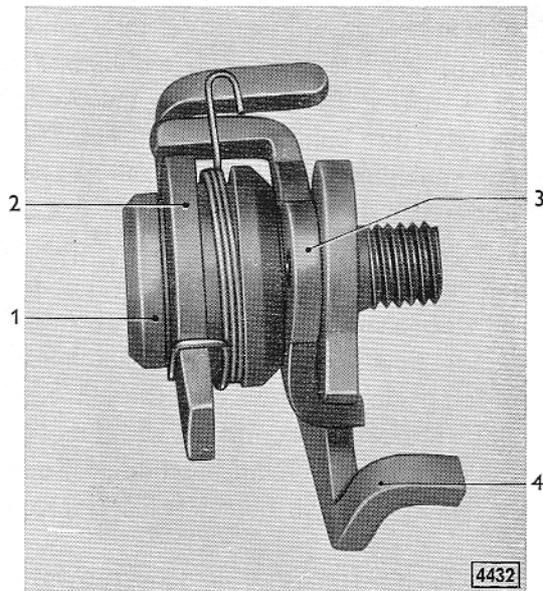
Zusammenbau Schnelleerlaufnocken mit Zusatzklappensperrhebel und unterem Luftklappenhebel
